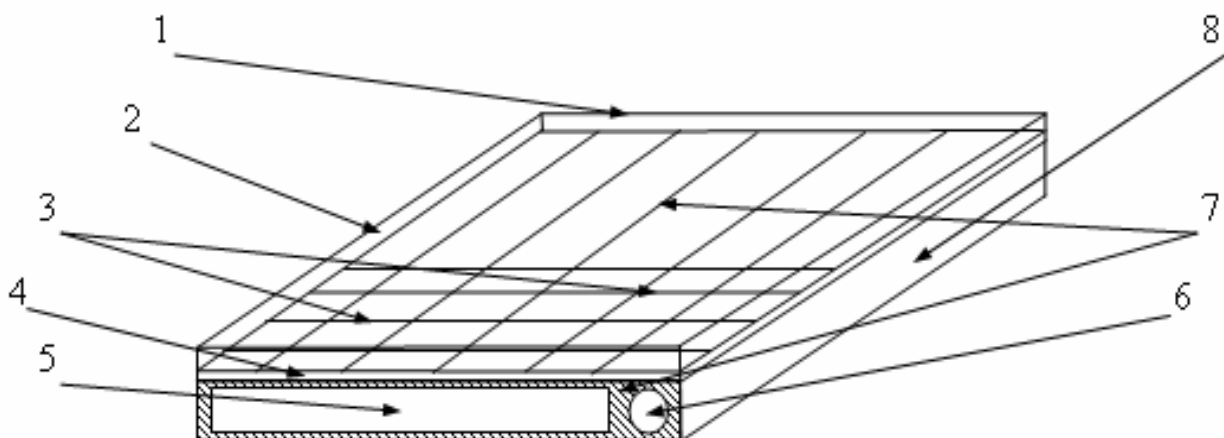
Схема пристрою комбінованої фотогеліустановки: 1 - верхнє зашклення; 2 - бічні кріплення для скла; 3 - сонячні елементи; 4 - ізоляційна плівка; 5 - повітряний канал; 6 - канал для води; 7 - геліопрофіль; 8 – корпус.
